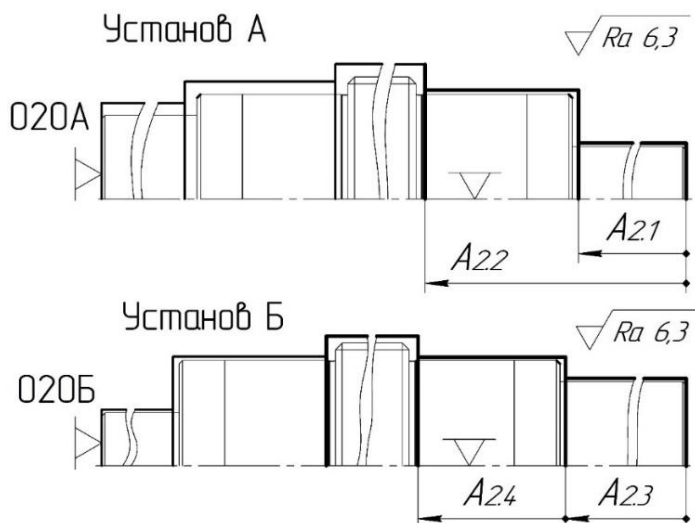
Ескіз заготовки на операції 020 «Токарна з ЧПК»
